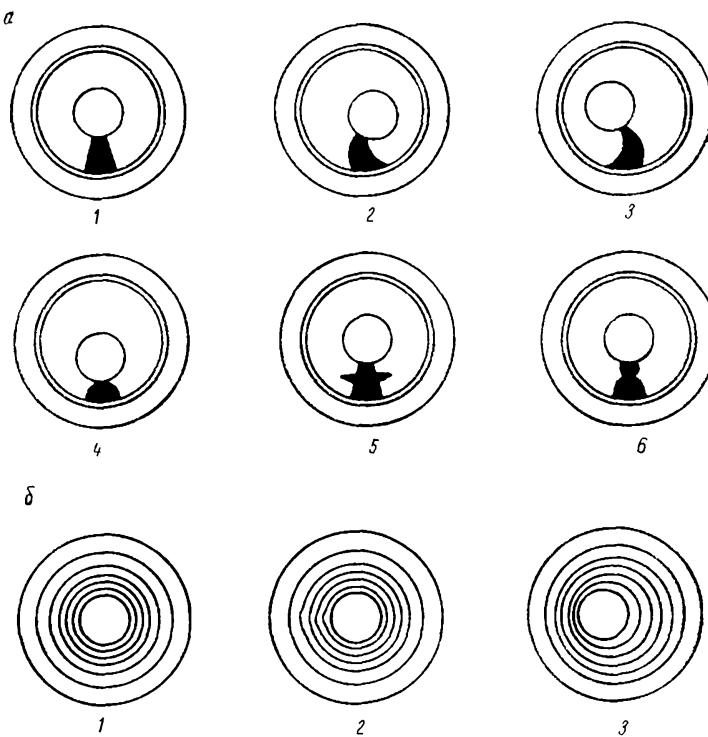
Обнаружение дефектов сверловки канала ствола:
